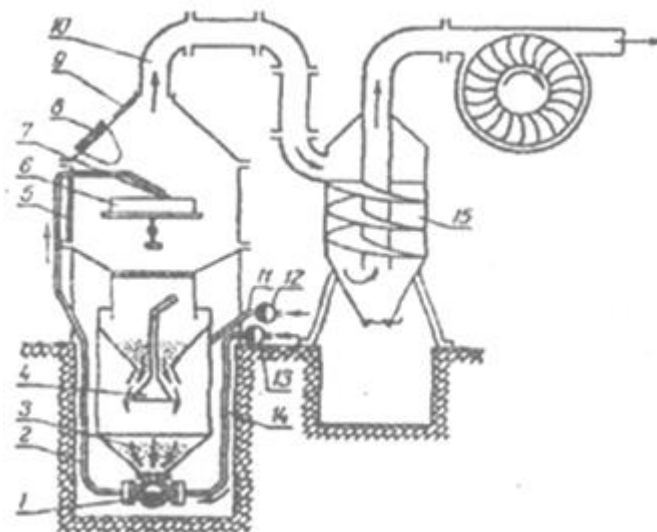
Схема установки для очистки деталей косточковой (металлической) крошкой
